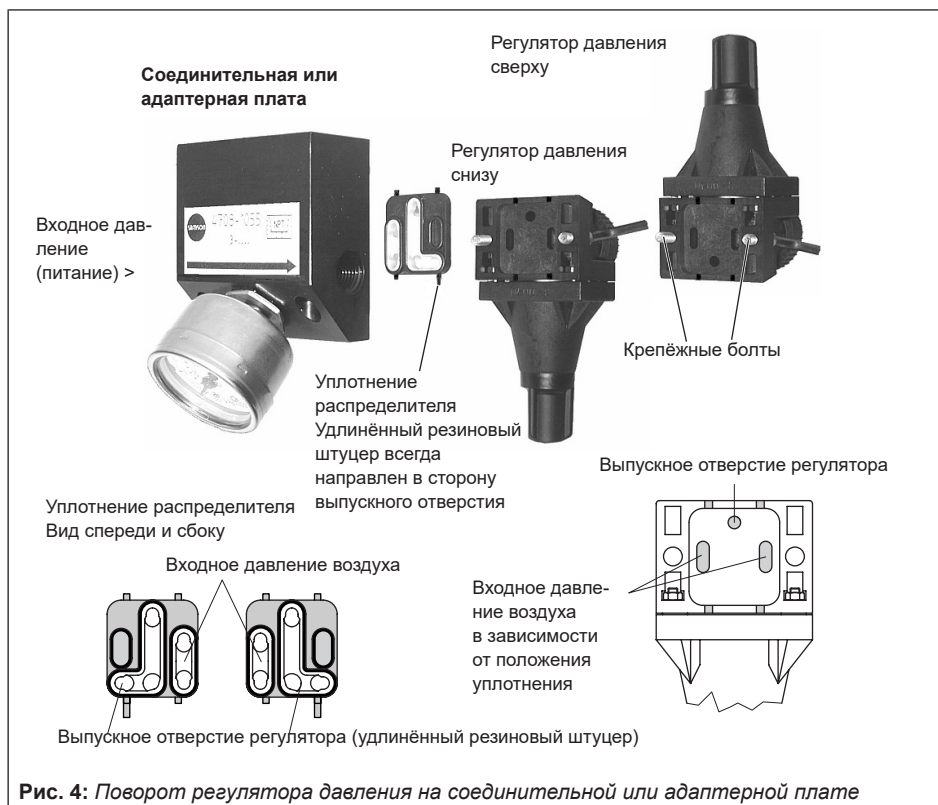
Поворот регулятора давления на соединительной или адаптерной плате
